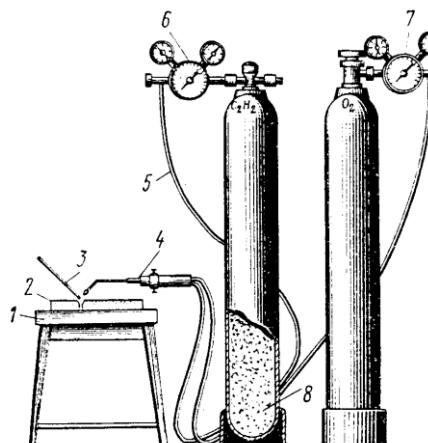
Схема поста газовой сварки с питанием от баллонов:
